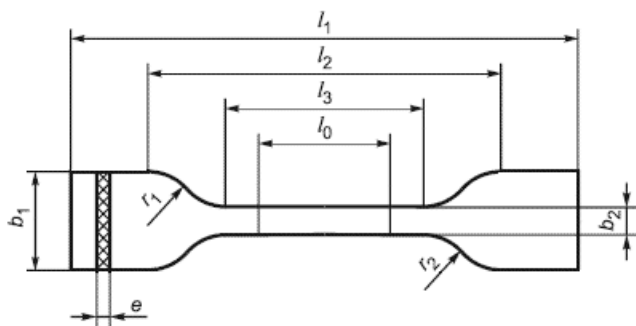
Образец типа 1, изготавливаемый вырубкой штампом-просечкой
